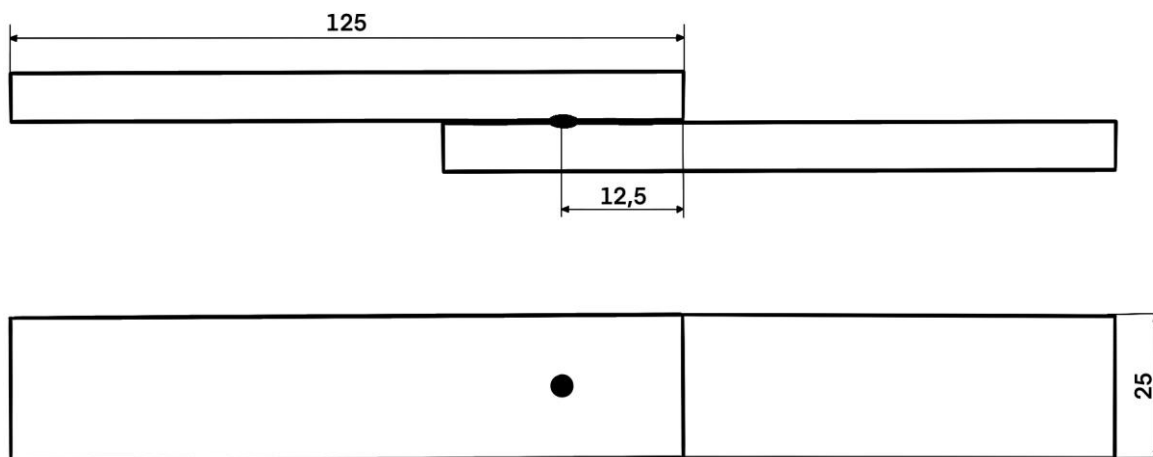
Representação esquemática da realização da soldadura das chapas com um ponto de soldadura
